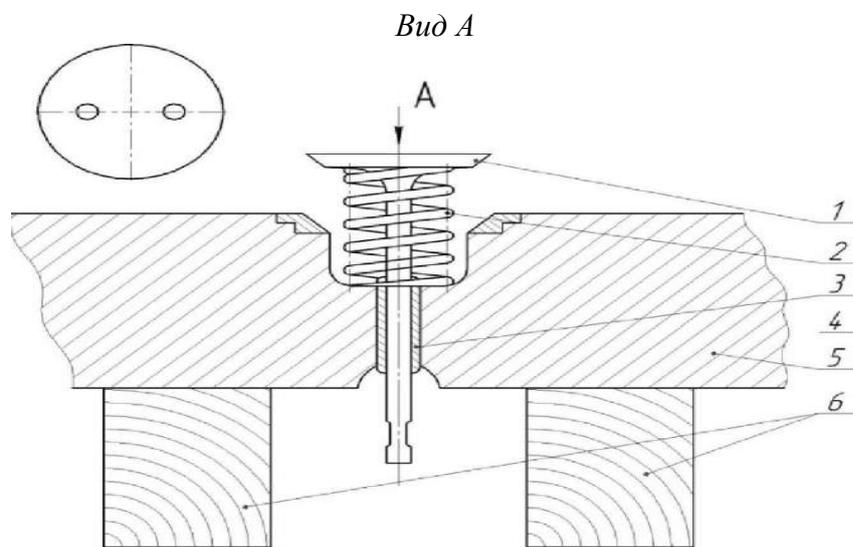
Притирка клапана к седлу 1 - Клапан; 2 - Пружина клапана; 3 - Направляющая втулка; 4 - Приспособление для притирки клапана; 5 - Крышка цилиндра; 6 - Стойки для установки крышки цилиндра
